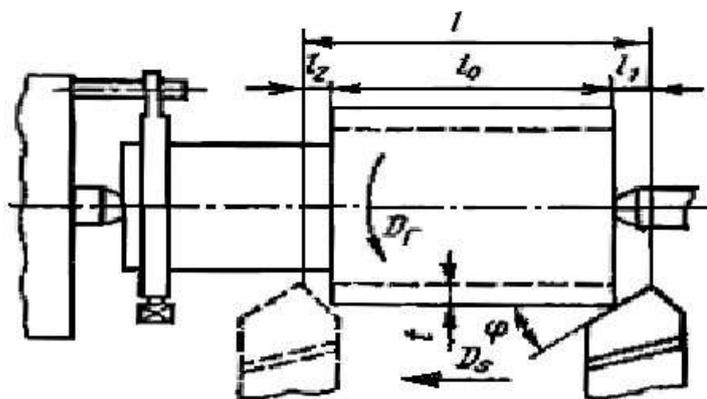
Схема к расчёту T_0 при обработке цилиндрической поверхности
